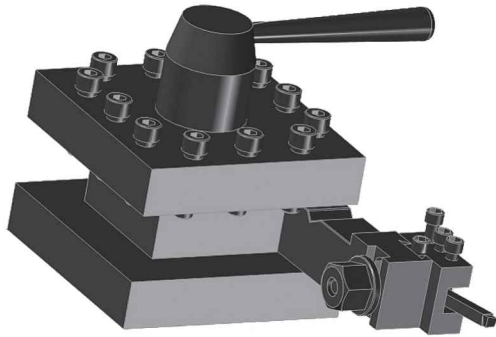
Isométrico para el montaje de torreta, portaherramienta y buril
